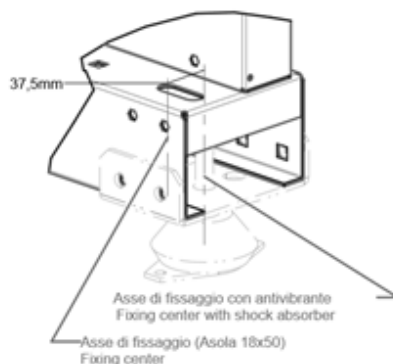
Particolare di fissaggio del traverso inferiore. Il traverso può essere fissato direttamente alla struttura di sostegno o se richiesto, con l'ausilio di un antivibrante opzionale nei casi in cui sia necessario ridurre la trasmissione delle vibrazioni e rumore.
